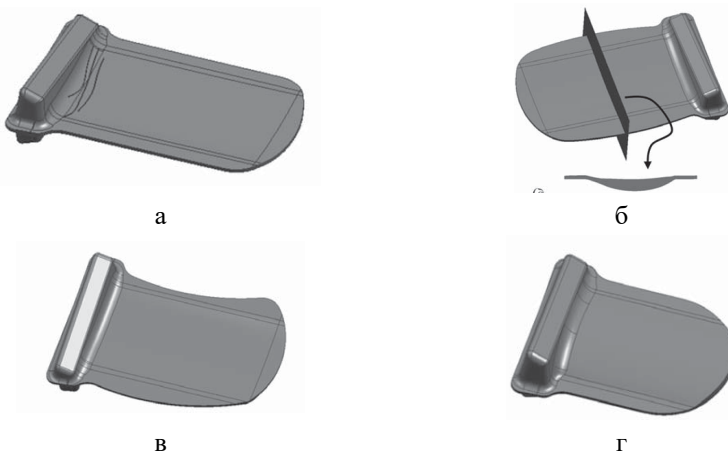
Основні види дефектів під час вальцювання заготовок лопаток газотурбінних двигунів зі штучної заготовки: а – тріщини в радіусі переходу замка в перо; б – задирка по краях пера заготовки; в – «шаблеподібність» пера заготовки лопатки; г – коротка вальцьована частина пера заготовки
